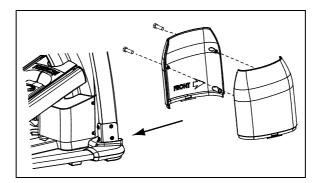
colocación de las cubiertas de los soportes verticales (se muestra cubierta derecha)
